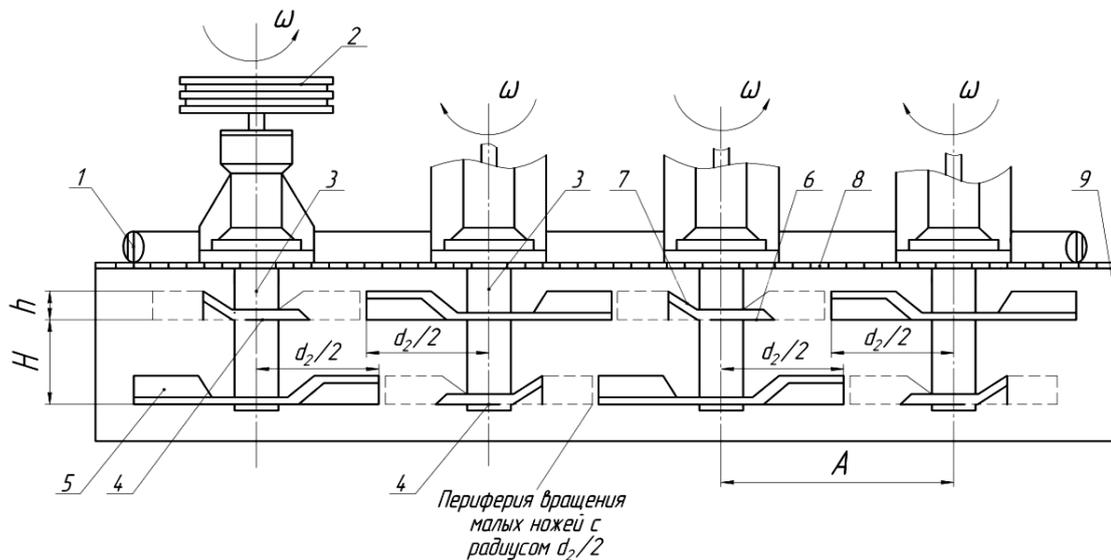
Роторный рабочий орган косилки-измельчителя сорной растительности: 1–рама; 2–привод; 3–вал; 4,5–ножи; 6,7–режущая кромка; 8–лист защитный; 9–полог
